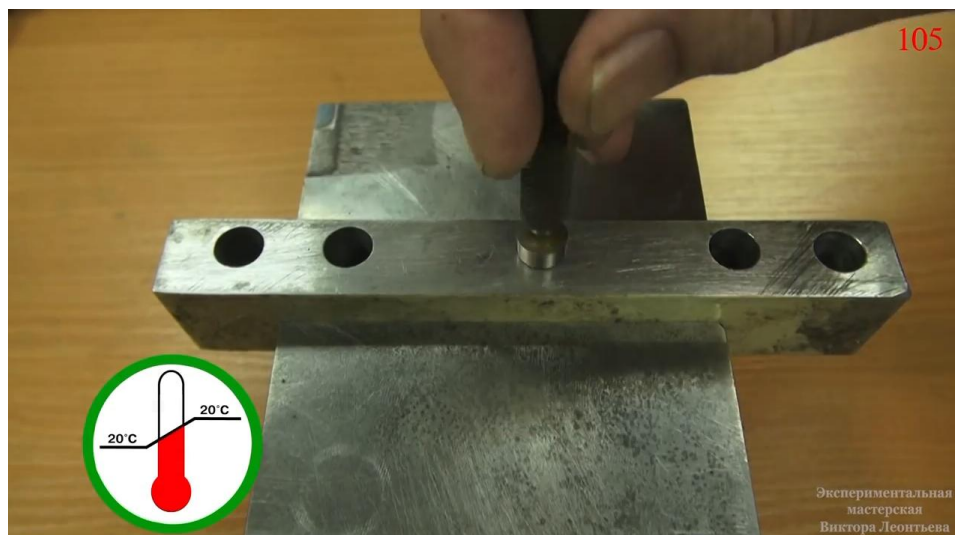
Пример проверки диаметра отверстий на детали с помощью калибра
